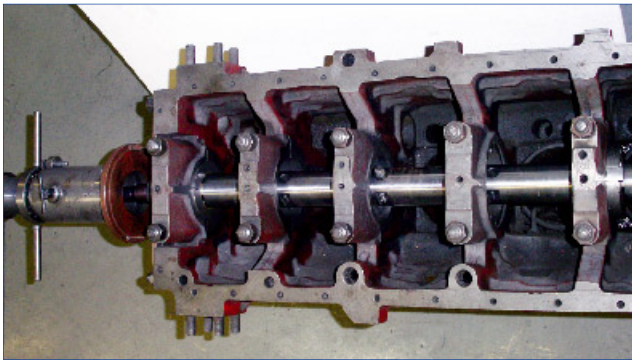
Борштанги для расточки и хонингования постелей коленчатого вала двигателя КамАЗ-740
